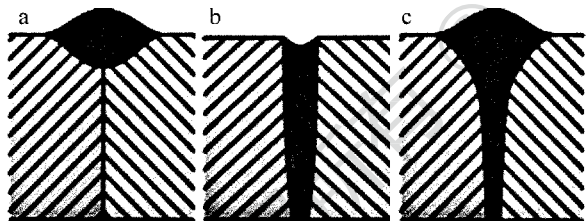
电弧焊接、激光焊接和复合焊接焊缝截面成型
